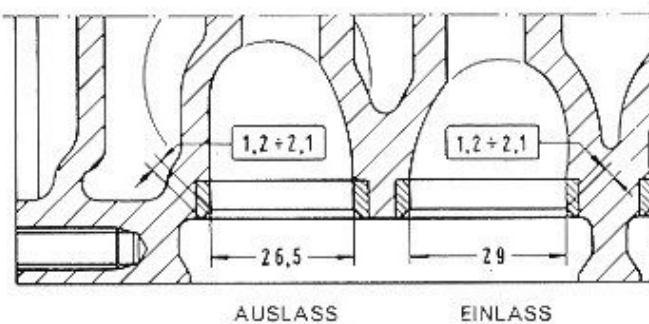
Die wichtigsten Angaben über die Ventilsitze im Zylinderkopf.
